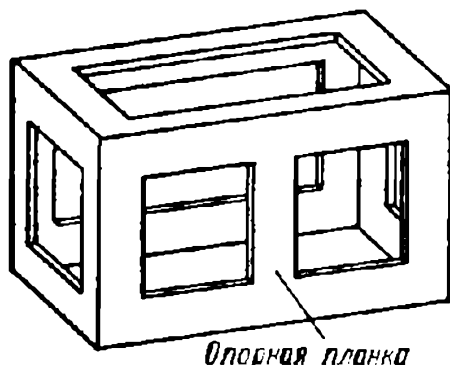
Деревянный каркас для сварки футеровки из листового свинца или пластика
